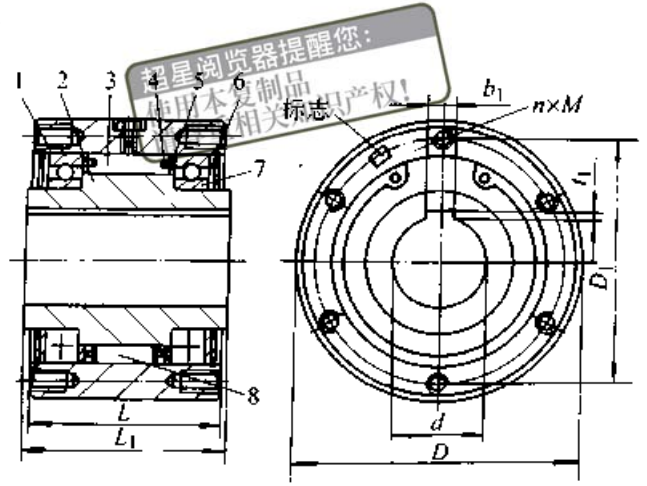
CKZ 型 (带轴承型) 单向楔块式超越离合器
